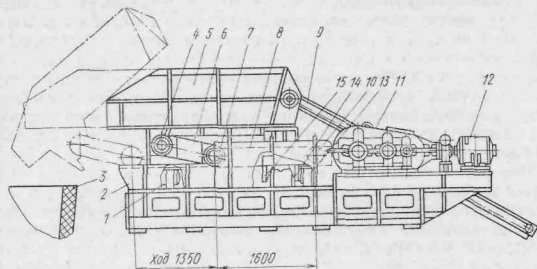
Машина для загрузки металлической сечки в сталеразливочный ковш
